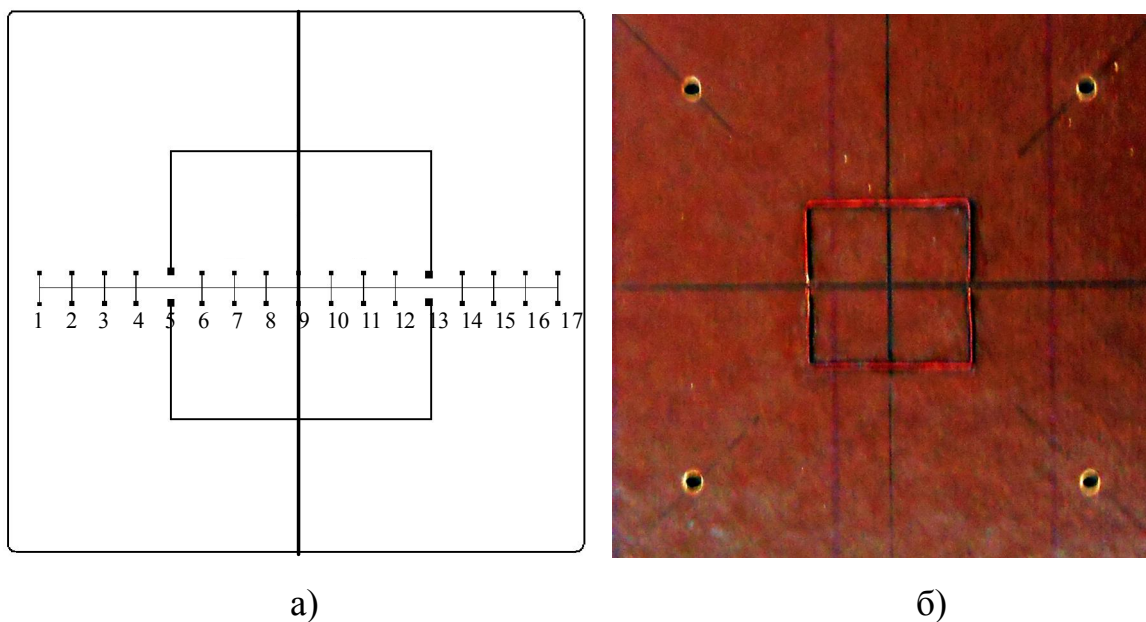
Индуктор с квадратным витком: а) схематическое изображение; б) экспериментальный образец
